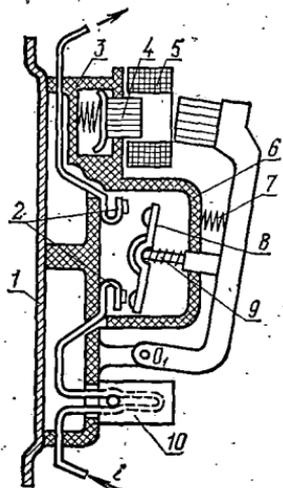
Схема магнитного пускателя серии ПАЕ:
